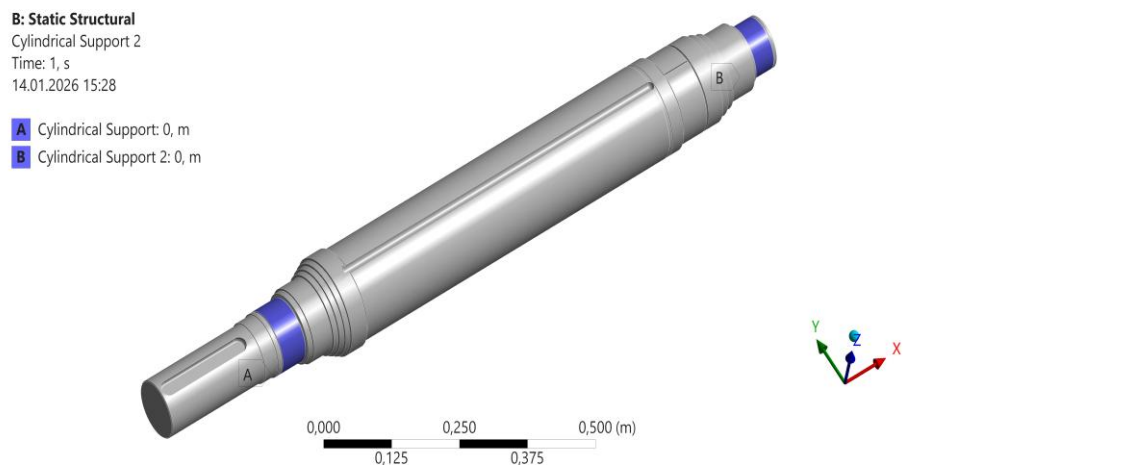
Схема закрепления ротора цилиндрическими опорами
